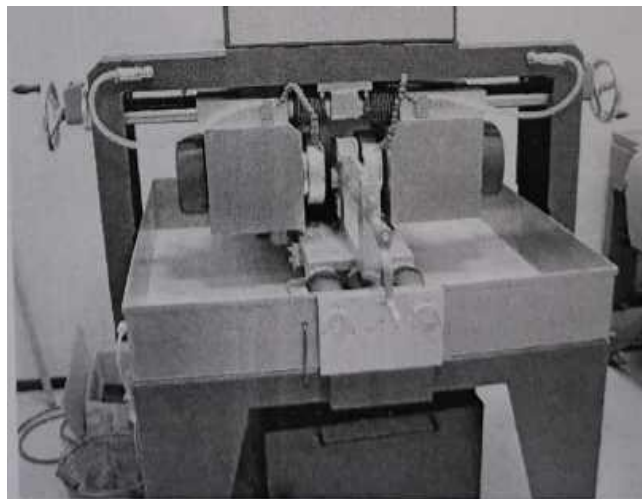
Шлифовальный станок STRASSENTEST Baustoff-Prufsysteme
